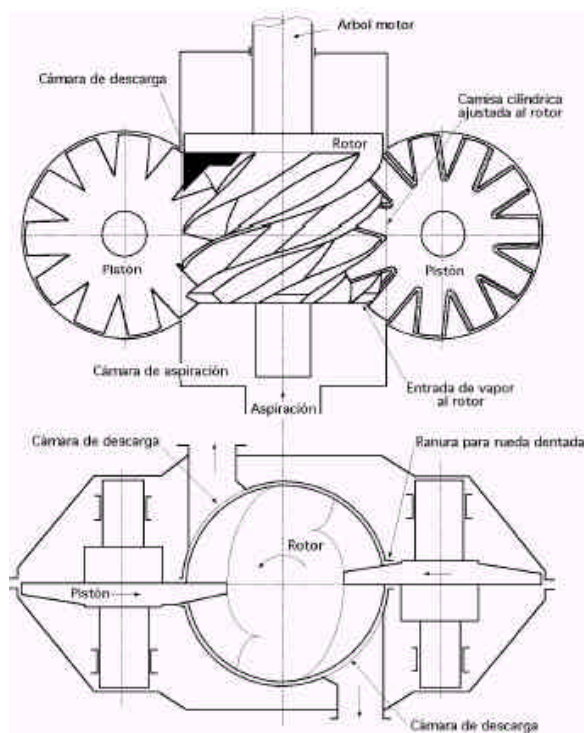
3. Esquema de un compresor de tornillo de dos rotores.
